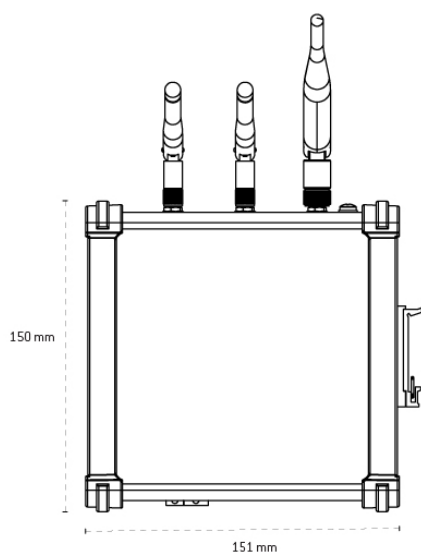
Dimensões do Universal IoT Gateway com caixa de alumínio
